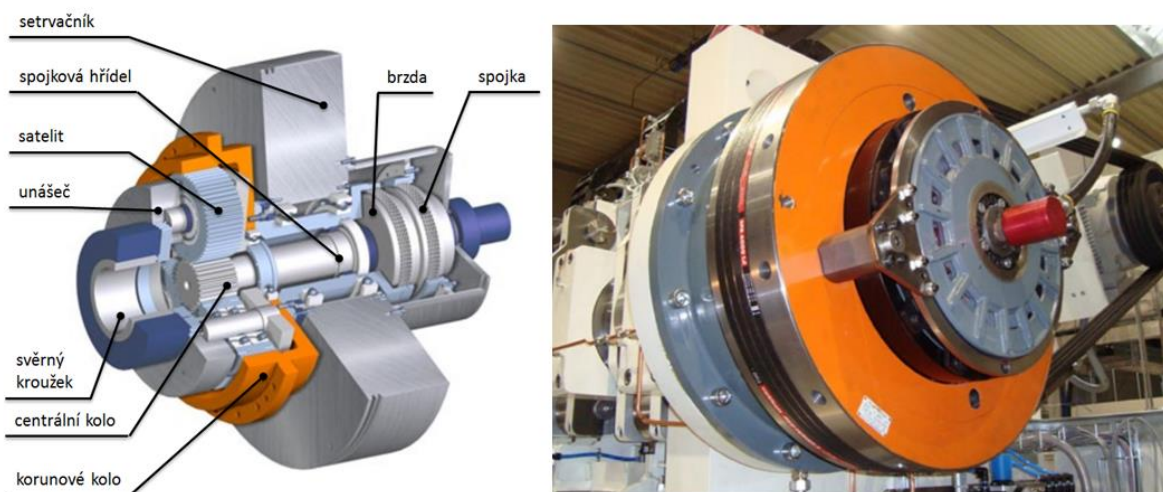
Pohonná jednotka DESCH Complete press drive HKB [34]
